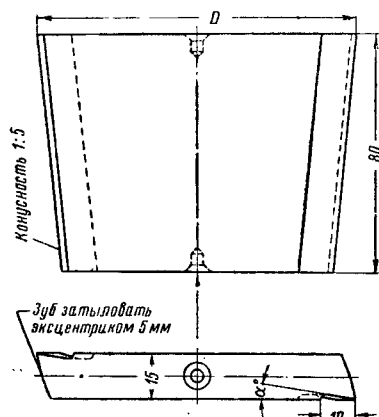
Развёртки с направлением для проверки конусов инжекторов типов В-170, В-250:
